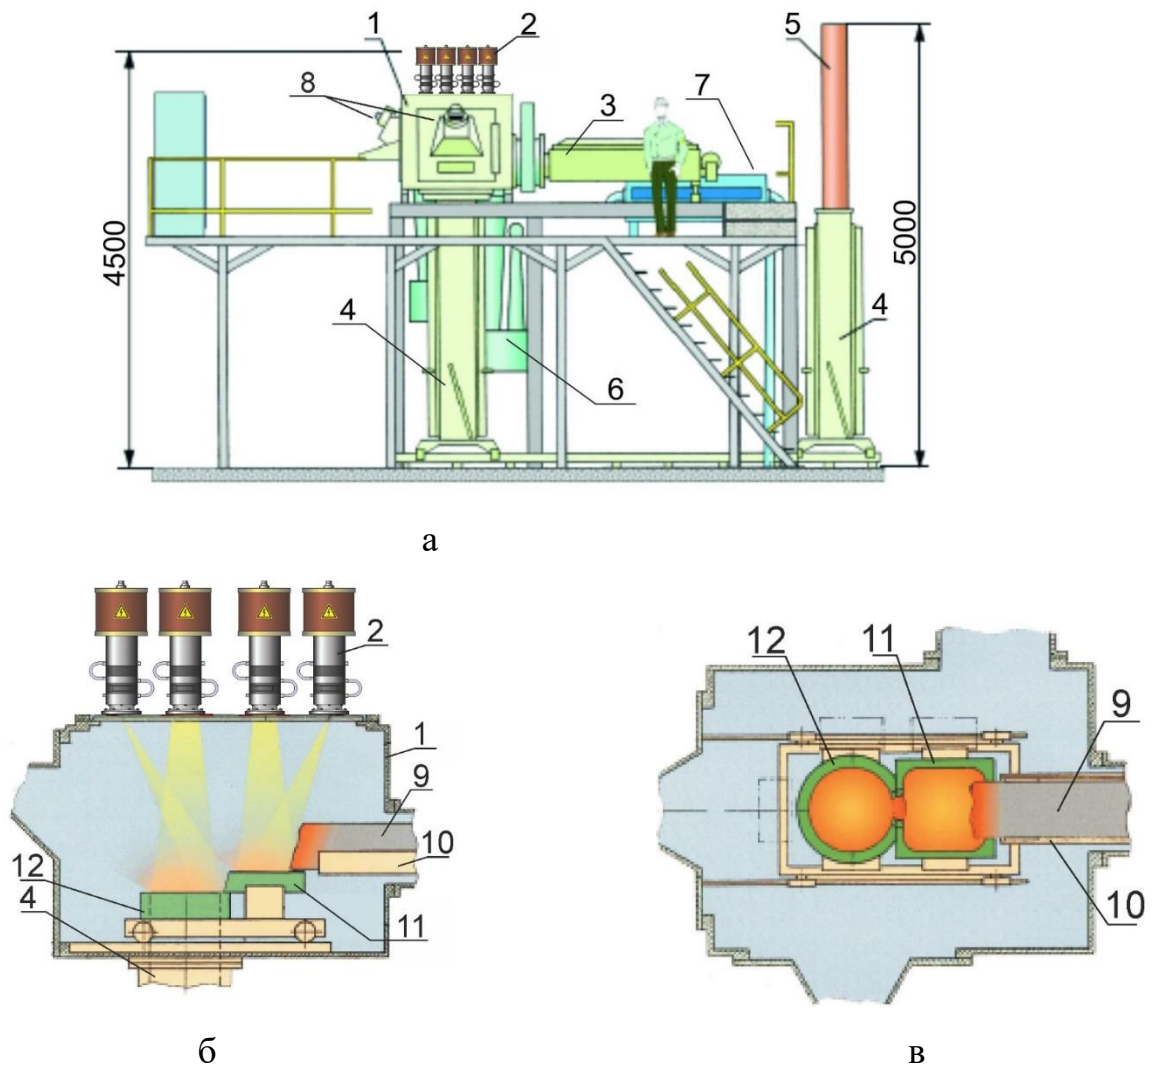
Схема загального виду установки L-4 (а); схема робочої камери (б, в): (1 - робоча камера; 2 - електронні гармати; 3 – завантажувальна камера з механізмом подачі шихти; 4 - механізм витягування зливка; 5 - зливоч; 6 - паромасляні насоси вакуумної системи; 7 – гідроблок системи охолодження; 8 - оглядові системи; 9 - матеріал, що переплавляється; 10 - висувний лоток; 11 - проміжна ємність; 12 – кристалізатор)
